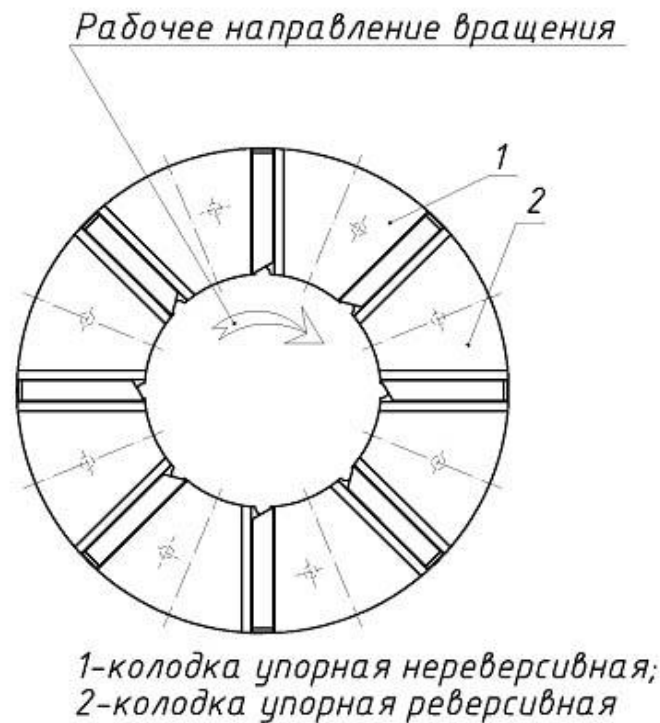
Упорний підшипник з реверсивними і нереверсивними колодками
